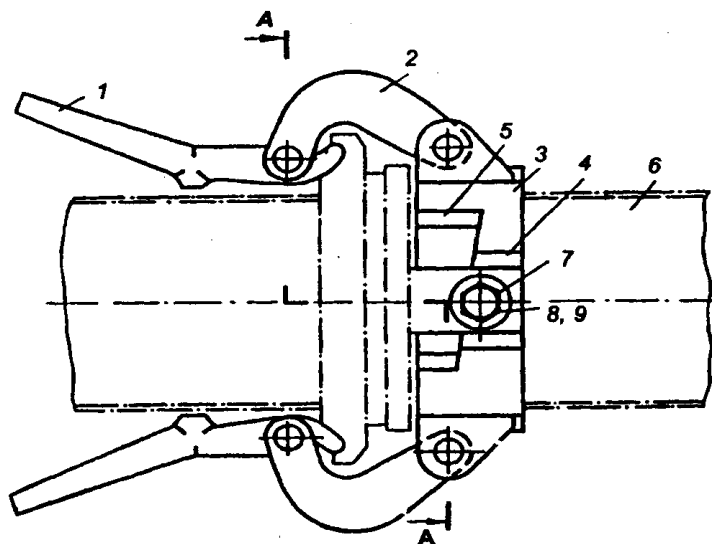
Двухрычажный быстроразъемный замок: 1 – рычаг; 2 – серьга; 3 – хомут; 4 – упорная планка; 5 – клин; 6 – звено; 7 – болт; 8, 9 – шайбы
